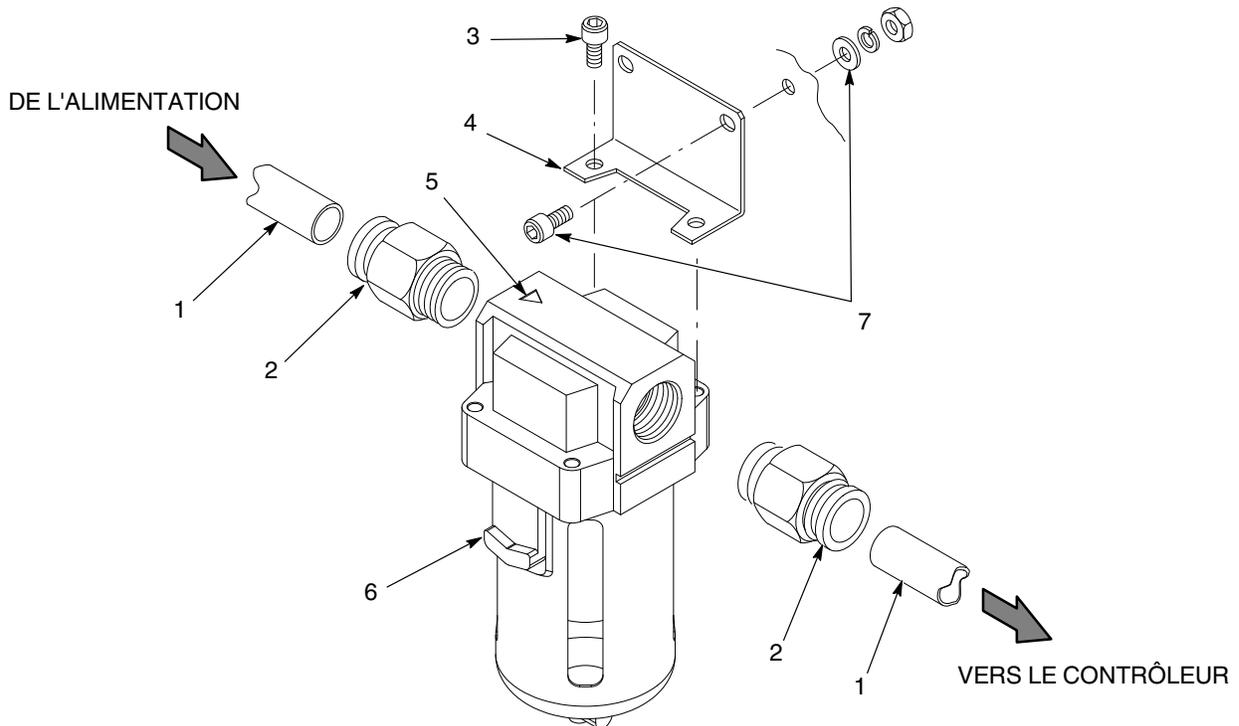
Installation du filtre à air – Systèmes à montage mural et sur rail
